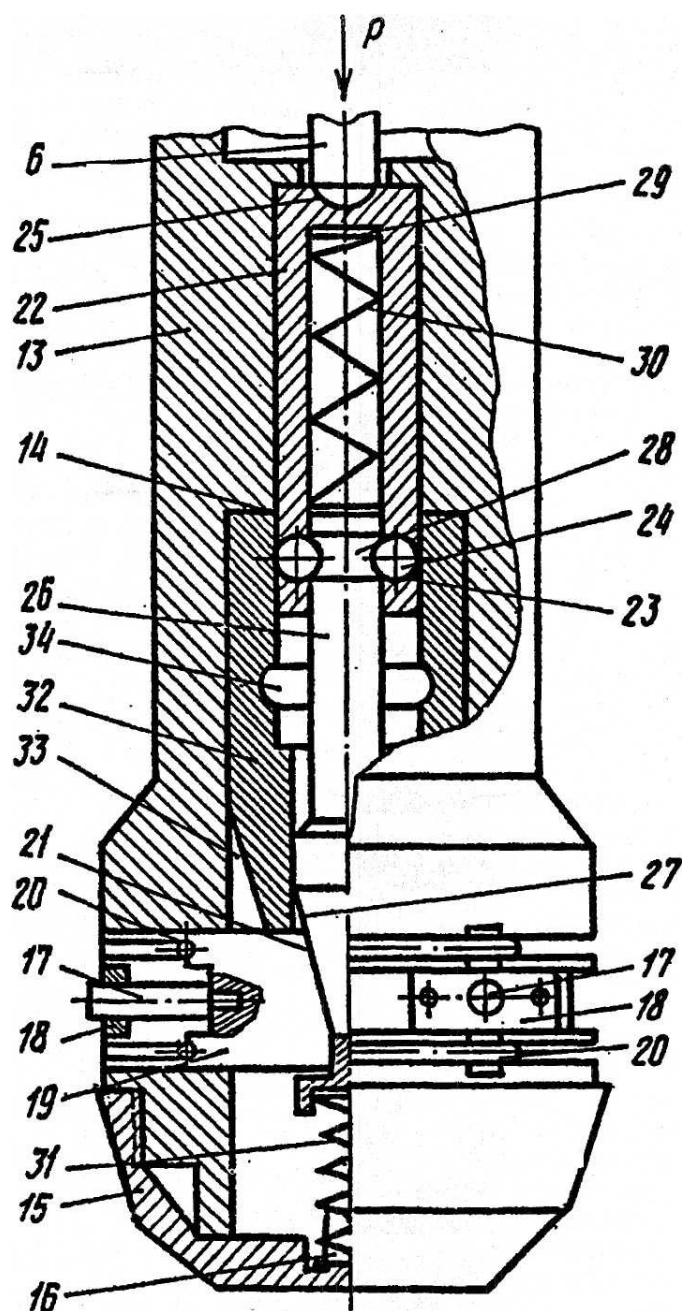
Рабочий инструмент станка для ФАБО цилиндров
